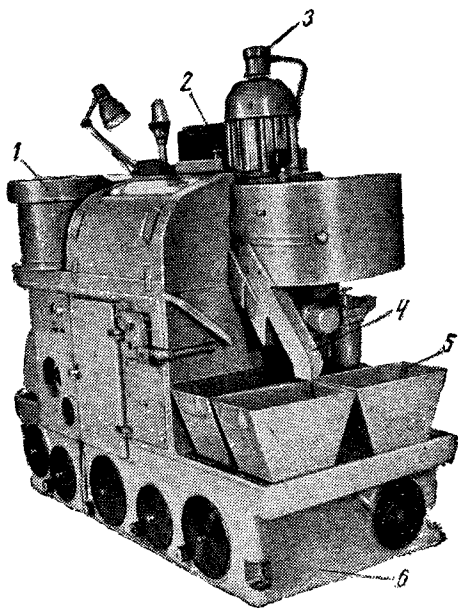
Непрерывно-протяжной автомат с движением детали ДТГ-2:
